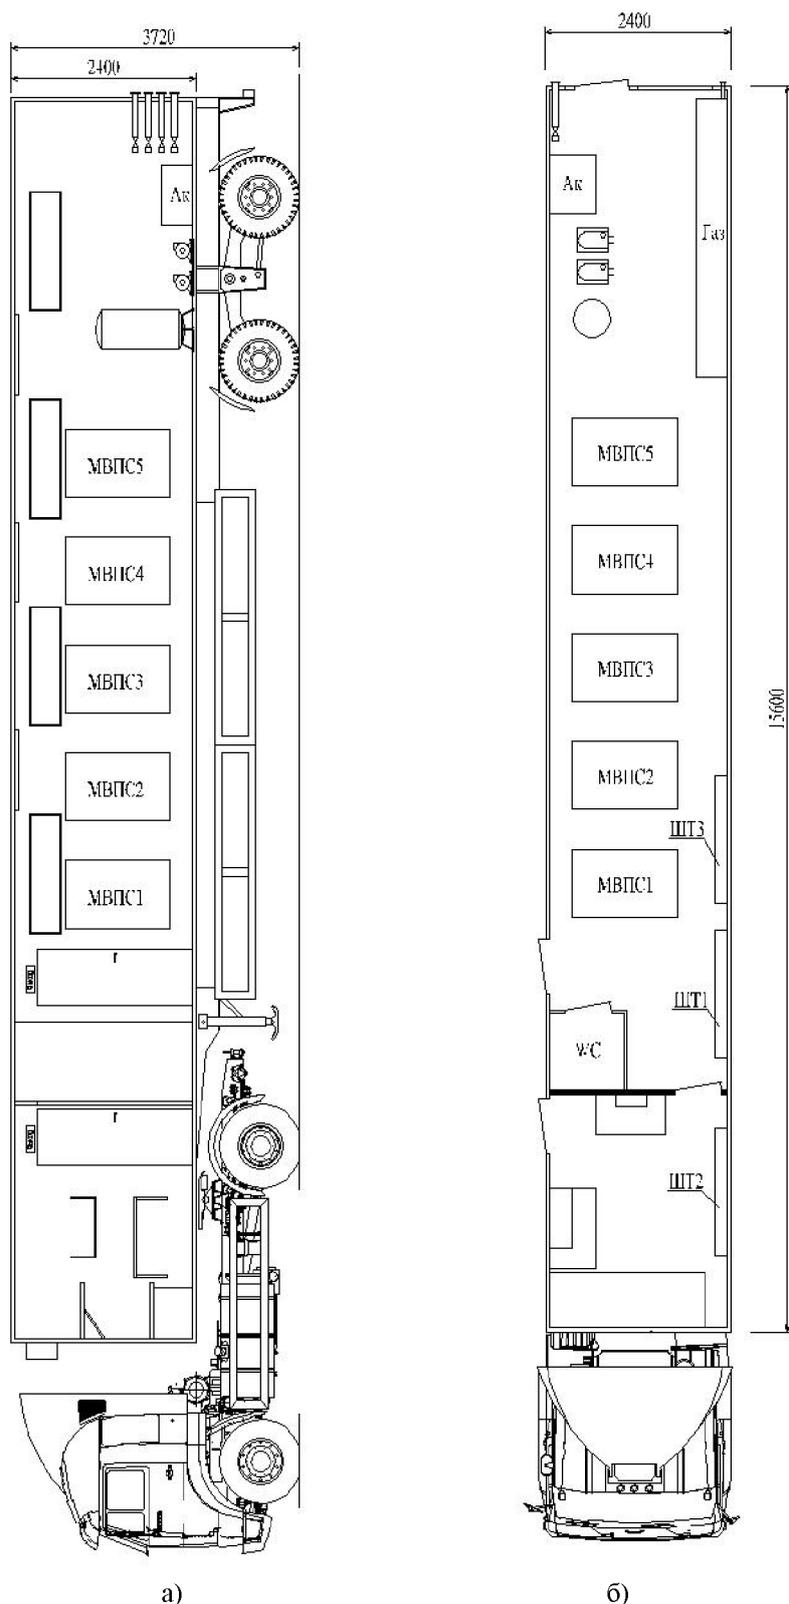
КАМАЗ (а – вид сбоку; б – вид сверху)
